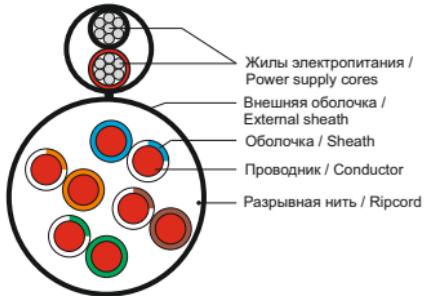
Конструкция кабеля типа U/UTP (с кабелем питания) / Figure 5 – Cable design of U/UTP type (with power supply cable)
